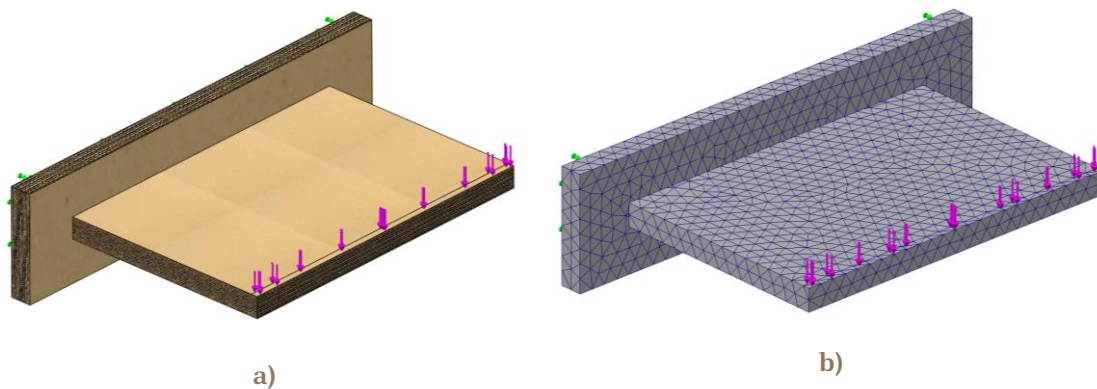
Unión plancha + horizontal tipo caja y espiga: a) configuración del ensayo de carga estática, b) malla generada || Fuente: Elaboración propia
